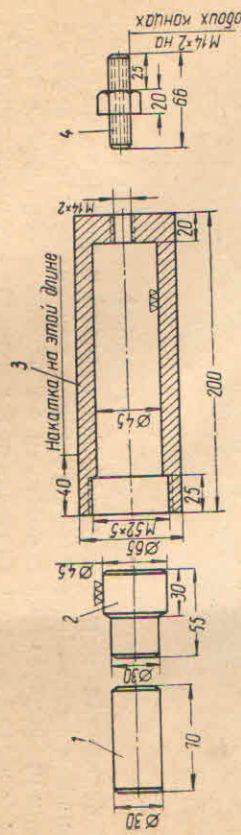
Стакан приспособления для заполнения пресс-форм сырой резиной: 1 — удлинитель; 2 — поршень; 3 — стакан; 4 — штупер
